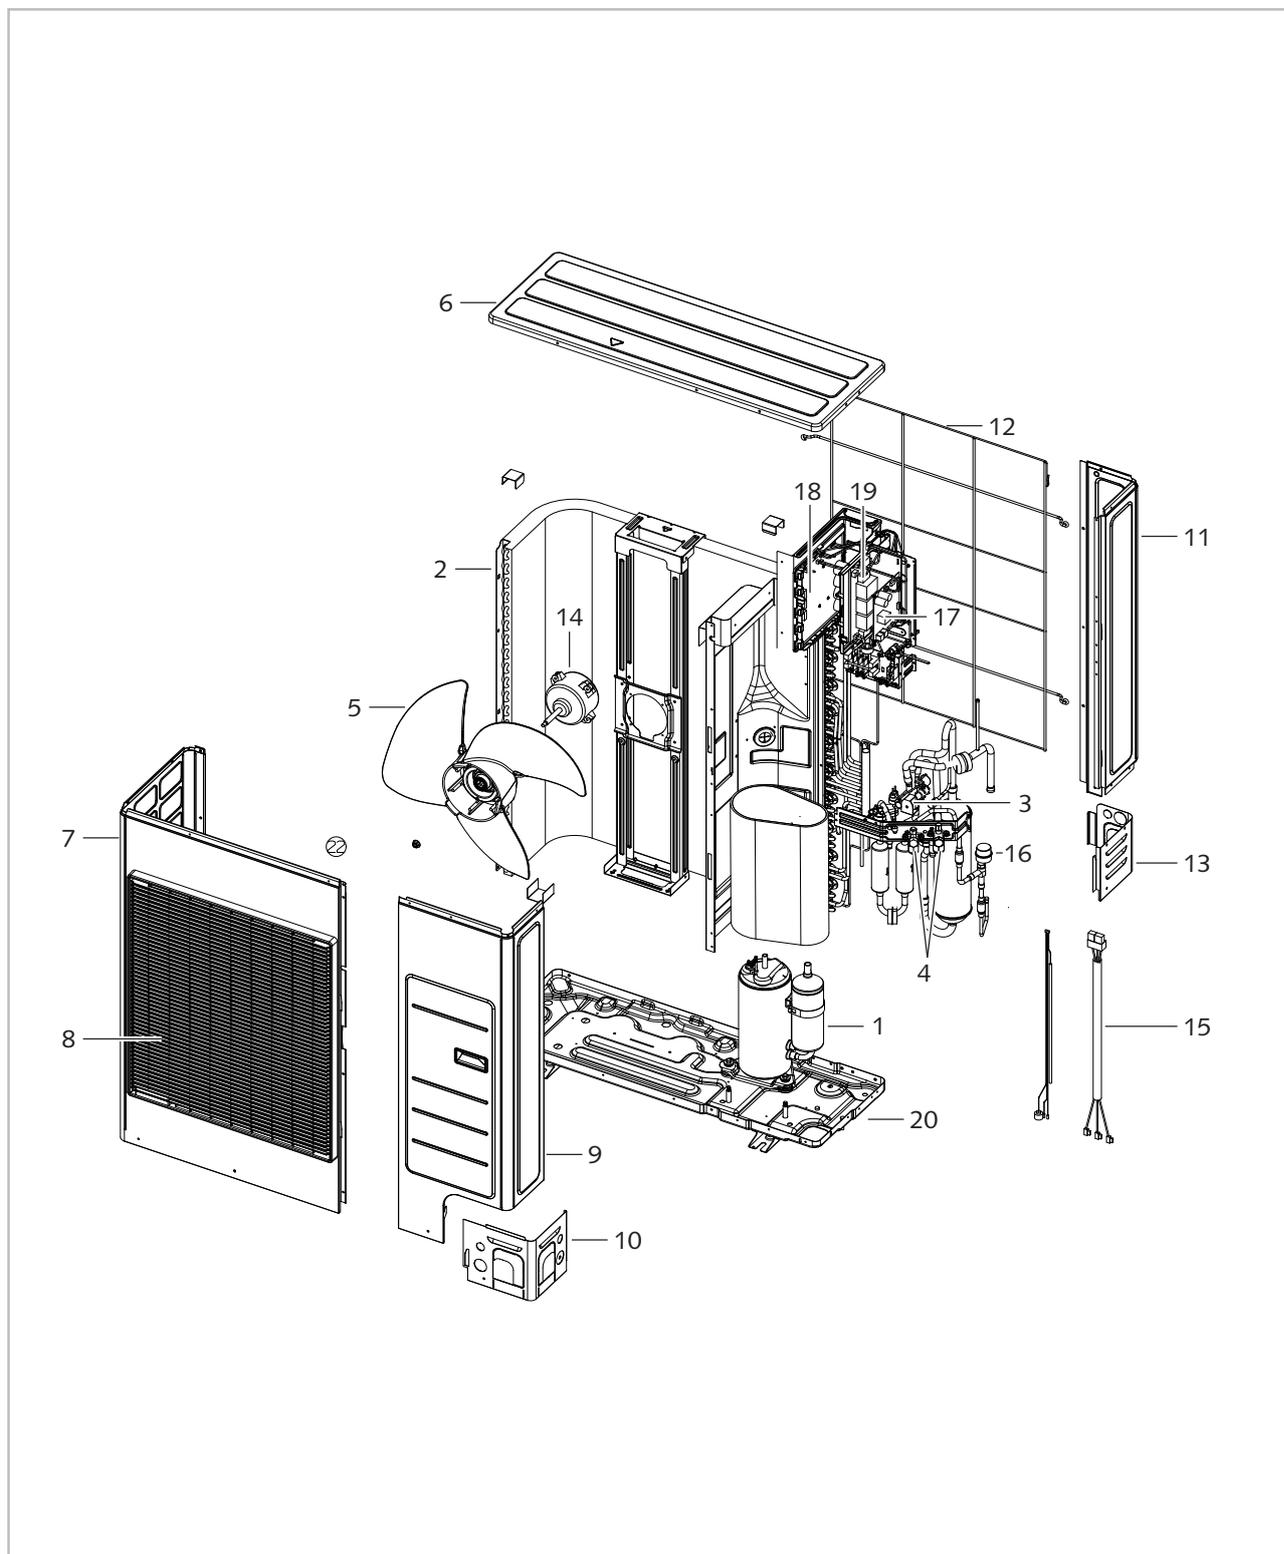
Vue éclatée du module externe WKF/WKF-compact 120
